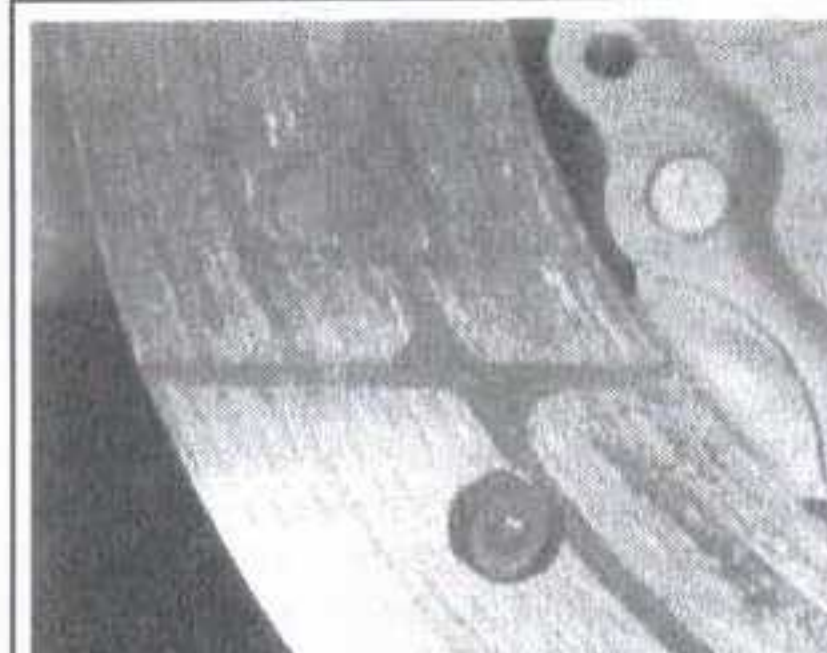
Проверьте диск сцепления на наличие неравномерного износа
